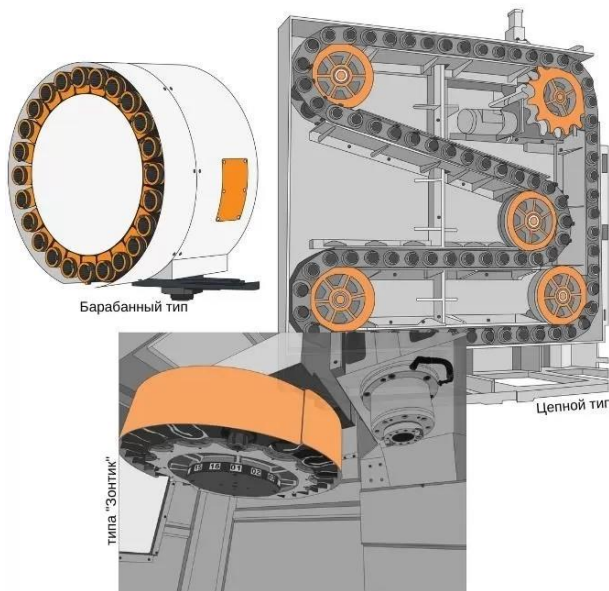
Різні варіанти виконання інструментальних магазинів фрезерних верстатів
